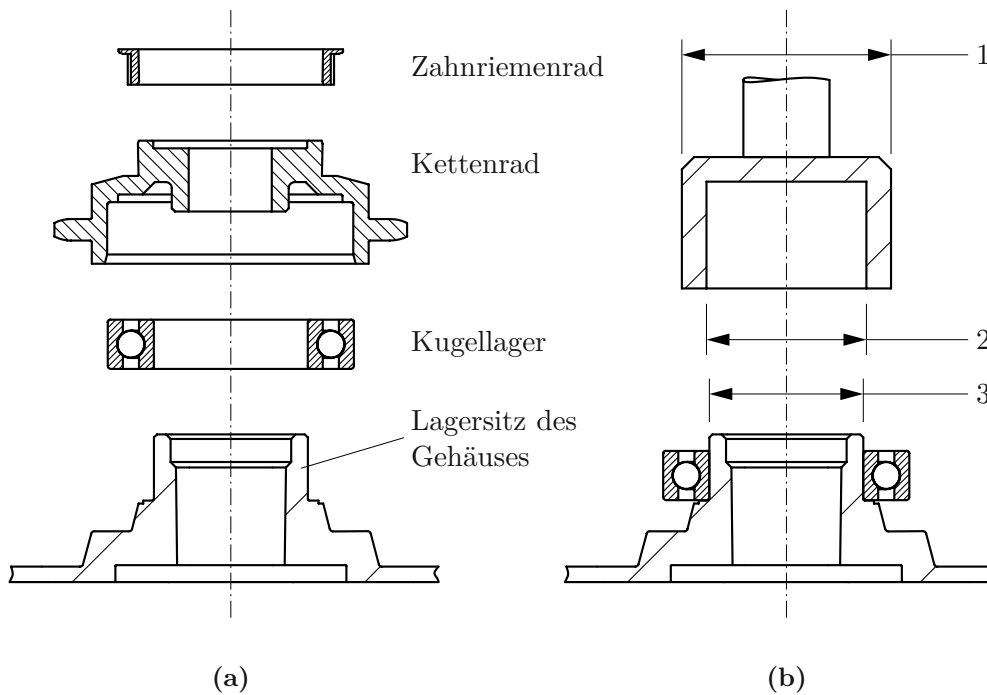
Pressvorgänge. Kritische Durchmesser: 1. Außendurchmesser des Stempels, 2. Innendurchmesser des Stempels, 3. Außendurchmesser des Lagersitzes
